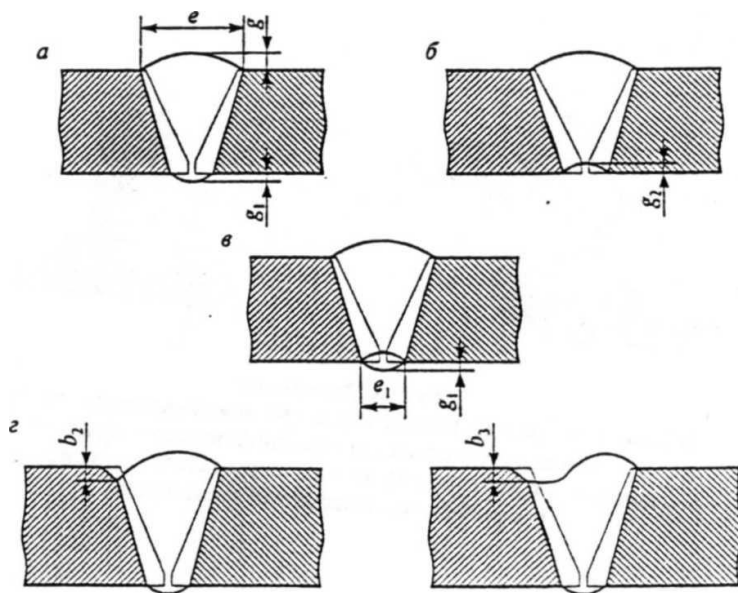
Конструктивные элементы и дефекты сварного шва, подлежащие измерительному контролю (начало): *а, б* – размеры (ширина, высота) стыкового одно-стороннего шва с наружной и внутренней стороны; *в* – то же двухстороннего сварного шва; *г* – подрез и неполное заполнение разделки кромок
